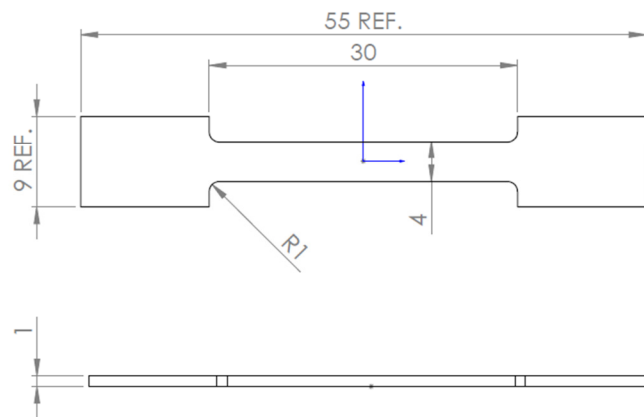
Desenho técnico do corpo de prova para ensaio de tração.
